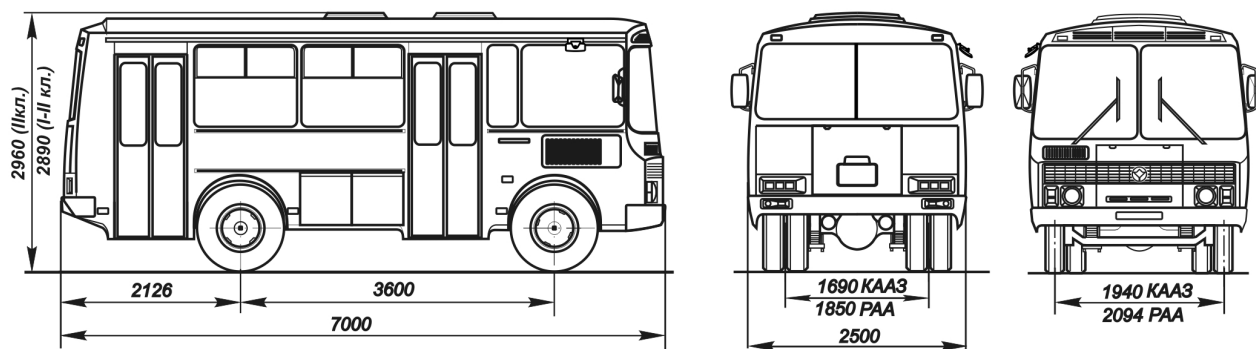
Габаритные размеры автобуса ПАЗ-32054-07
